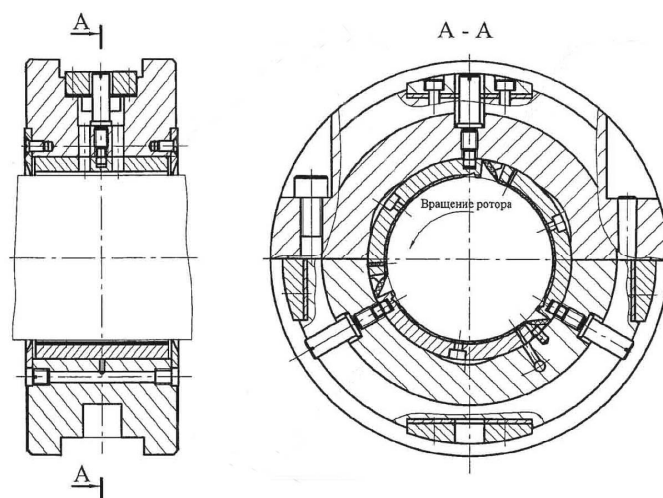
Конструкция подшипника ПД-120 турбины 103JT
